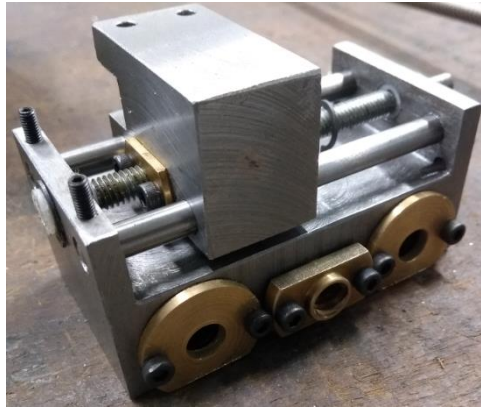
montagem dos carros transversal e longitudinal (Fonte: acervo próprio).
